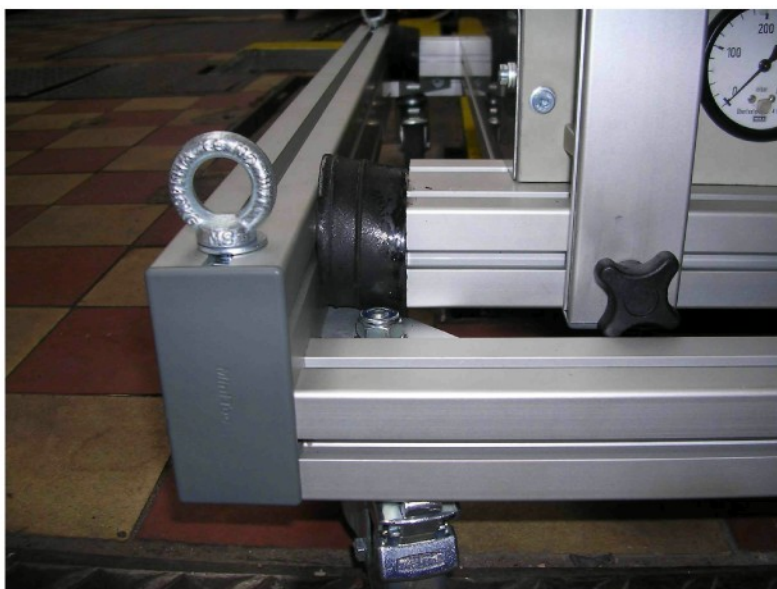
Smontovaná konstrukce – pohled ze strany vlnovce
